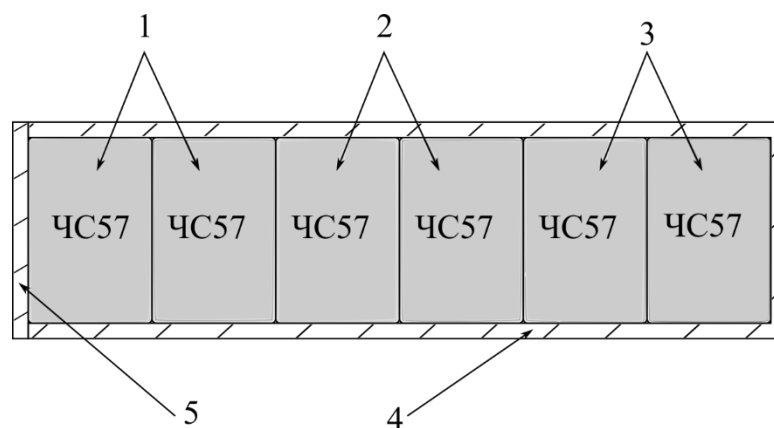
Схема укладки образцов в контейнер для последующей сварки методом горячего изостатического прессования: 1 - 3 - стальные заготовки, обработанные соответственно по режимам 1, 2 и без лазерной обработки; 4 - тонкостенный контейнер, 5 - крышка контейнера.
